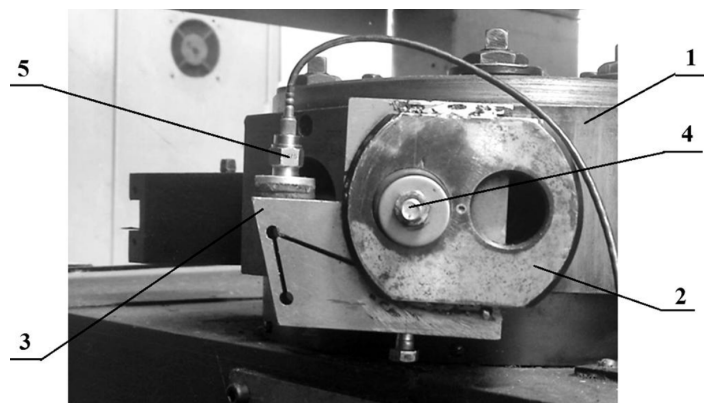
Різцетримач в робочій зоні верстата: 1 – револьверна головка; 2 – корпус різцетримача; 3 – пружна частина різцетримача; 4 – вісь демпфера; 5 – акселерометр мод. Д13
